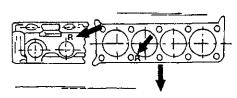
Расположение маркировки "R" на блоке цилиндров и на прокладке головки цилиндров.
